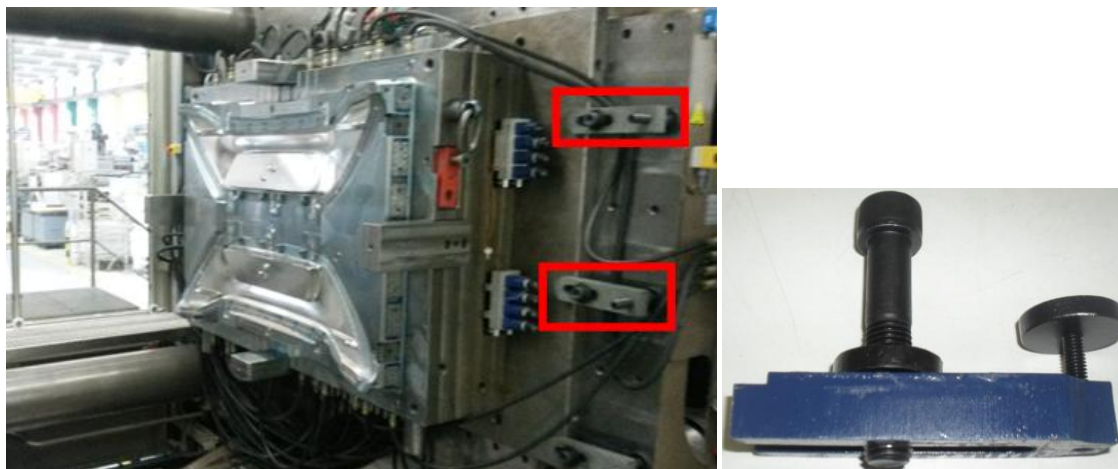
Cavidade de molde fixa na máquina de injeção (esquerda) e barra de fixação (direita) (IMA - Indústria de Moldes de Azeméis, 2013).
